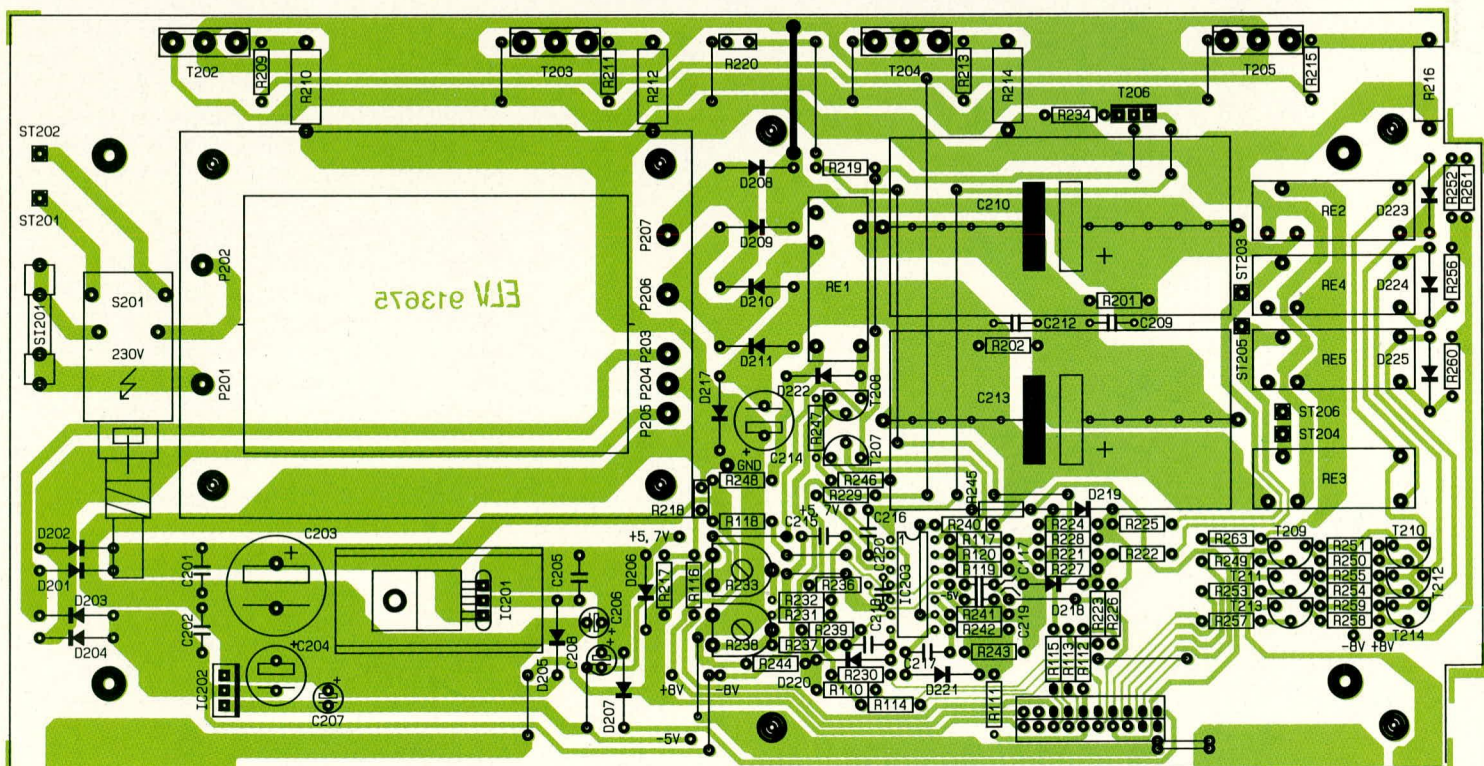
Bestückungsplan der Basisplatte. Die Leitungen an ST 203 - ST 205 werden günstigerweise schon vor dem Einlöten der benachbarten Bauelemente angeschlossen.
